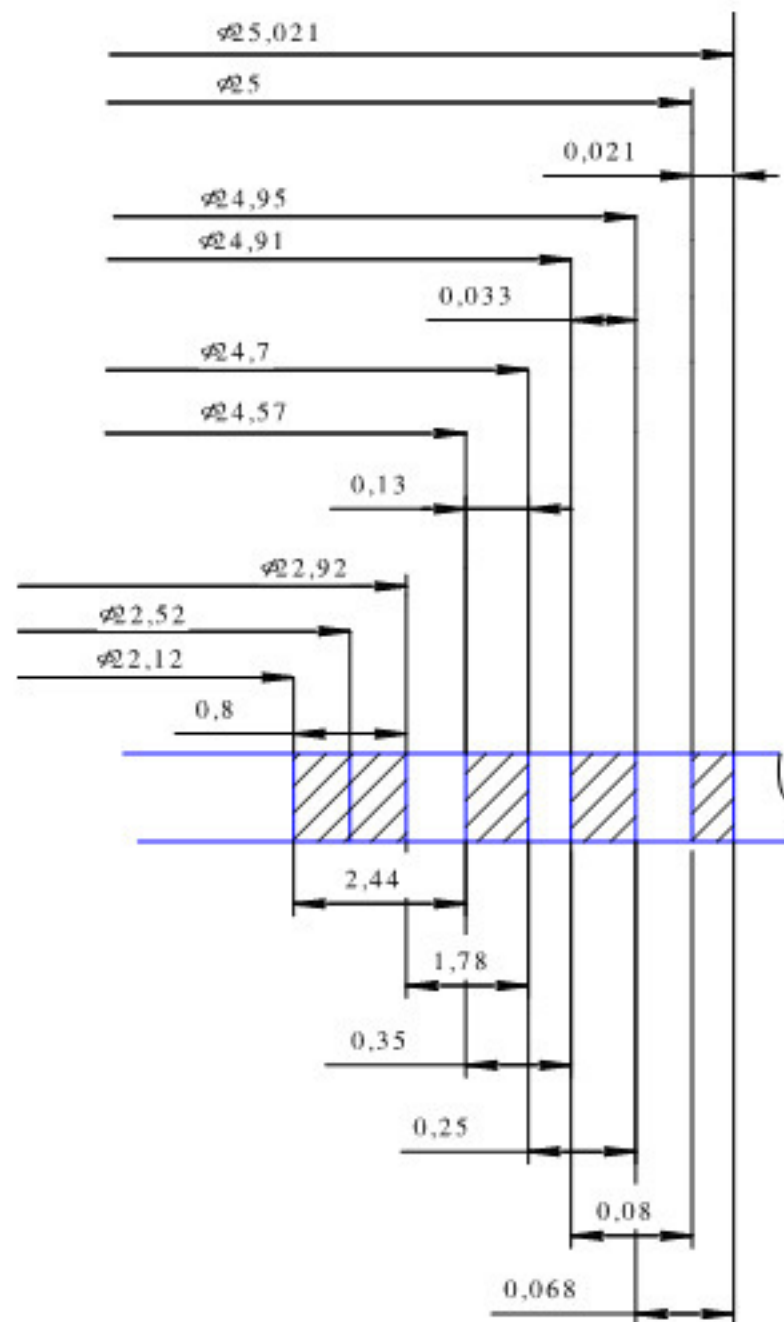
Схема графічного розташування полів припусків і допусків для обробки внутрішнього отвору $\varnothing 25H7^{(+0,021)}$
